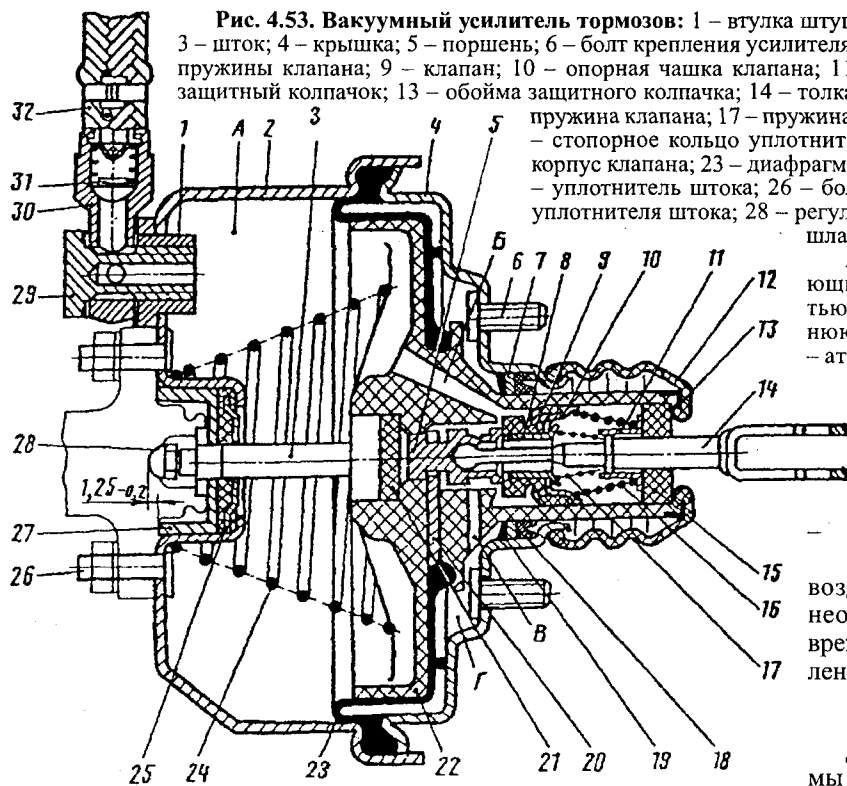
Вакуумный усилитель тормозов: 1 – втулка штуцера вакуумного шланга; 2 – корпус усилителя; 3 – шток; 4 – крышка; 5 – поршень; 6 – болт крепления усилителя; 7 – дистанционное кольцо; 8 – опорная чашка пружины клапана; 9 – клапан; 10 – опорная чашка клапана; 11 – опорная чашка возвратной пружины; 12 – защитный колпачок; 13 – обойма защитного колпачка; 14 – толкатель; 15 – воздушный фильтр; 16 – возвратная пружина клапана; 17 – пружина клапана; 18 – уплотнитель крышки корпуса; 19 – стопорное кольцо уплотнителя; 20 – упорная пластина; 21 – буфер; 22 – корпус клапана; 23 – диафрагма; 24 – возвратная пружина корпуса клапана; 25 – уплотнитель штока; 26 – болт крепления главного цилиндра; 27 – обойма уплотнителя штока; 28 – регулировочный болт; 29 – штуцер; 30 – наконечник шланга; 31 – клапан; 32 – шланг;
